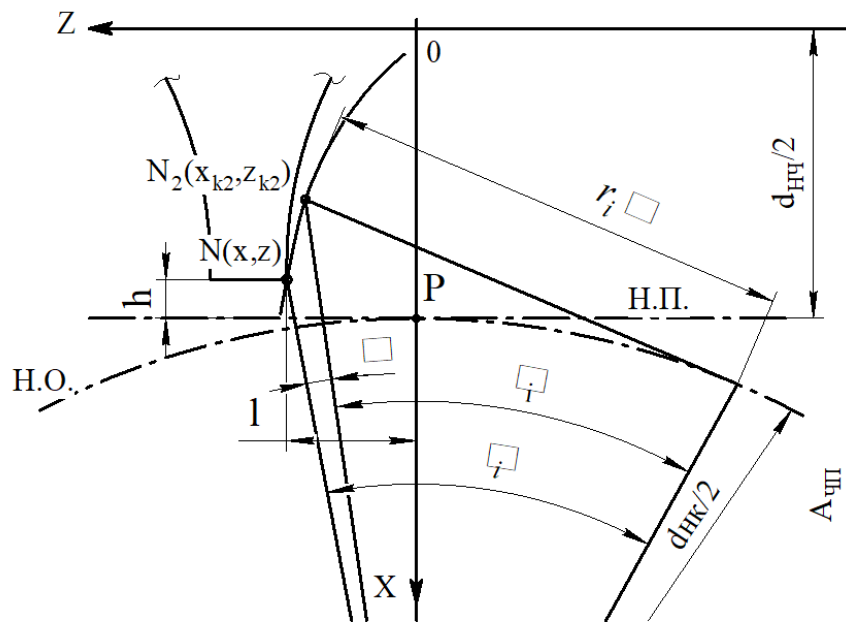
Схема к расчету профиля зуба червячного колеса образованная головкой зуба червячной фрезы
